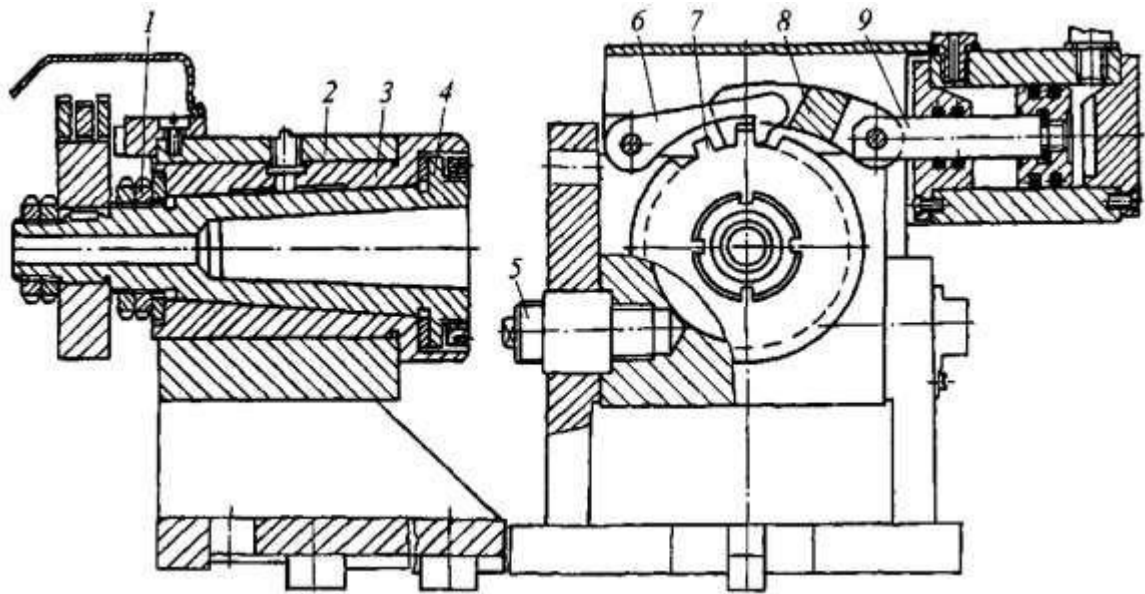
Поворотное устройство с управлением от пневмо- или гидропривода.
